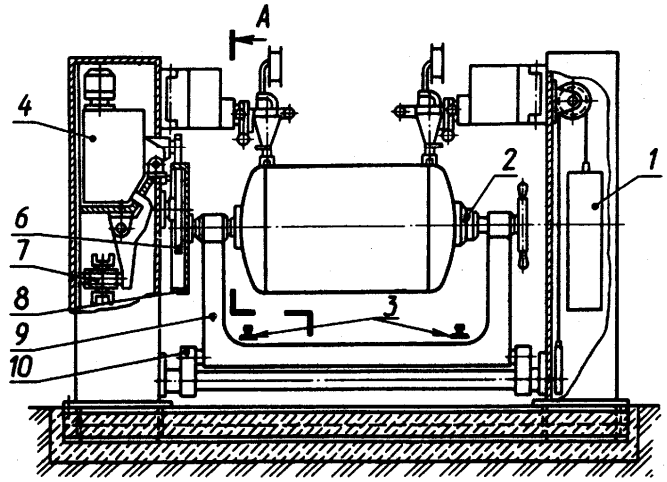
Стенд для автоматической сварки овальных сосудов
